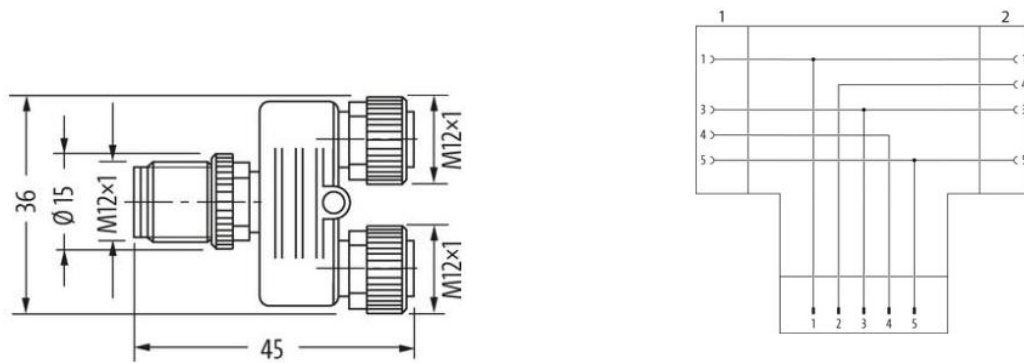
mechanische Dimension und Schaltplan Y-Connector
